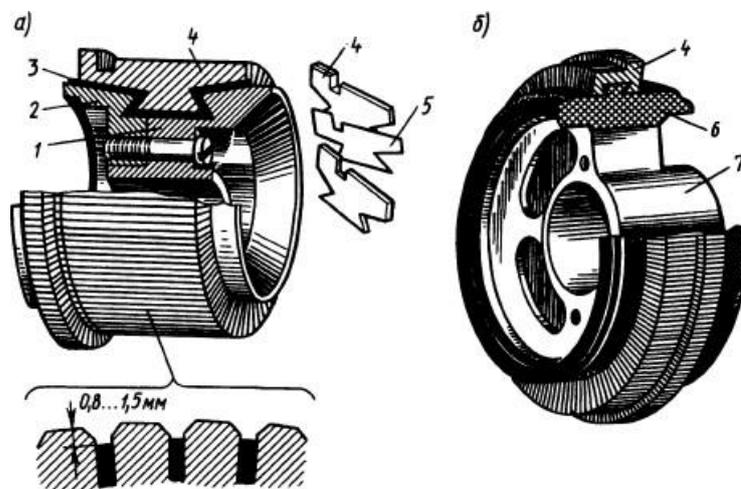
Устройство коллектора машины постоянного тока с металлическим (а) и пластмассовым (б) корпусом: 1 – корпус; 2 – нажимной фланец; 3 – изоляционные манжеты; 4 – коллекторные пластины; 5 – изоляционные прокладки; 6 – пластмасса; 7 – втулка
